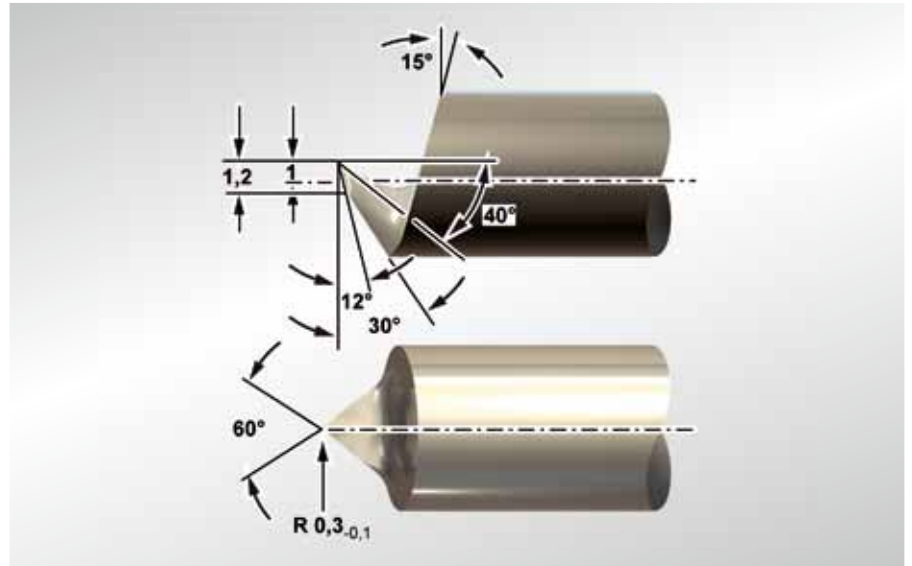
Schneidwerkzeug für Permaglide® P22 und P202
